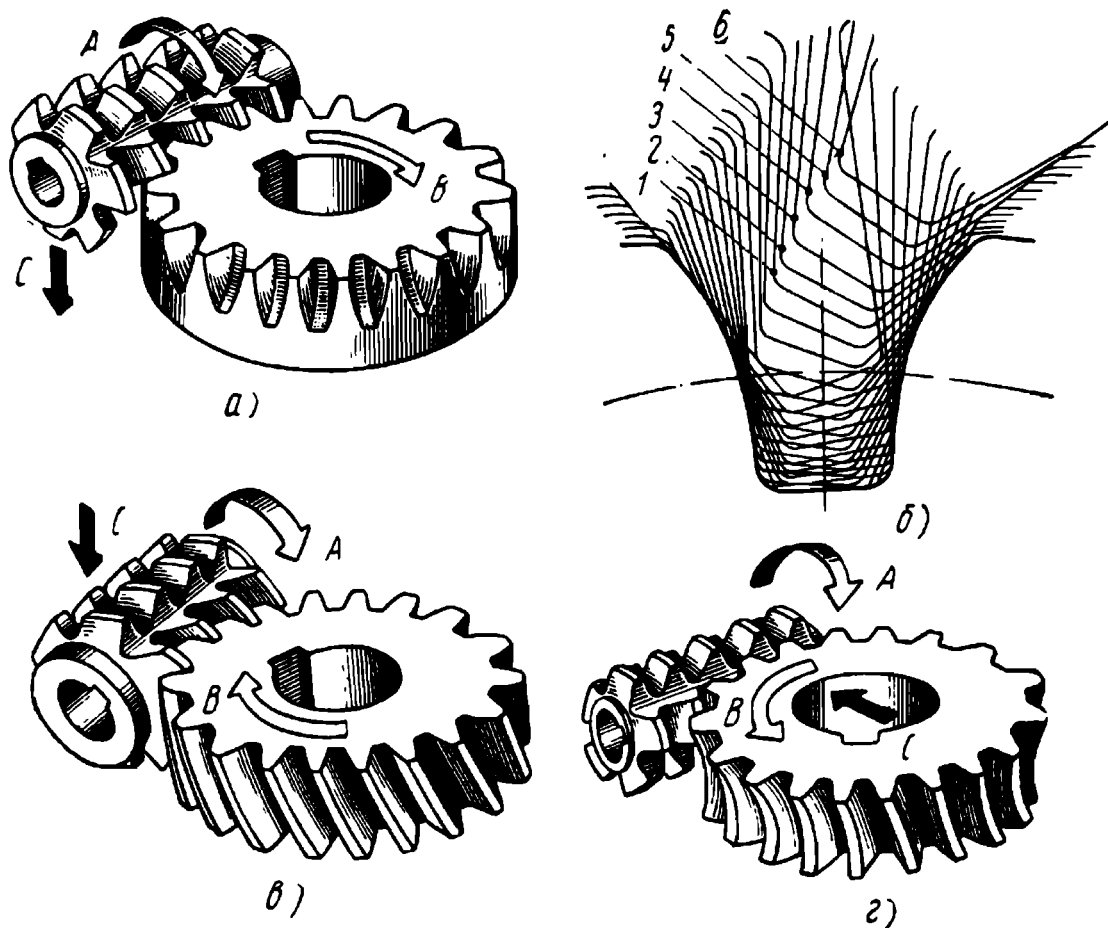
Схемы нарезания зубчатых колес по методу обкатки: а — цилиндрического колеса с прямыми зубьями, б — схема последовательного положения зубьев червячной фрезы при фрезеровании впадины зубчатого колеса, в — цилиндрического колеса с винтовыми зубьями, г — червячного колеса; буквой А обозначено направление вращения фрезы; В — направление вращения нарезаемой заготовки; С — направление подачи заготовки
